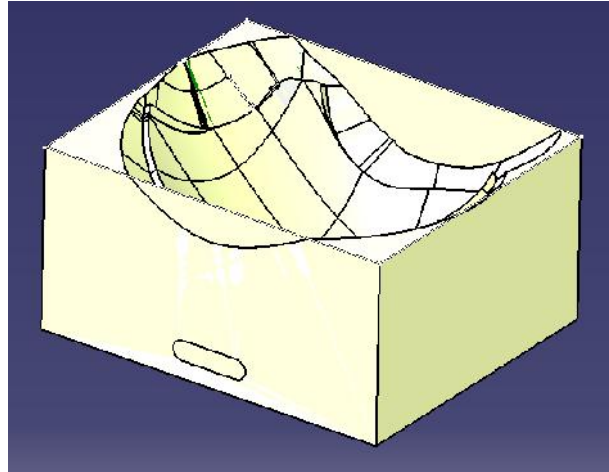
CAD del molde hembra previo al definitivo con creces de 1 mm
